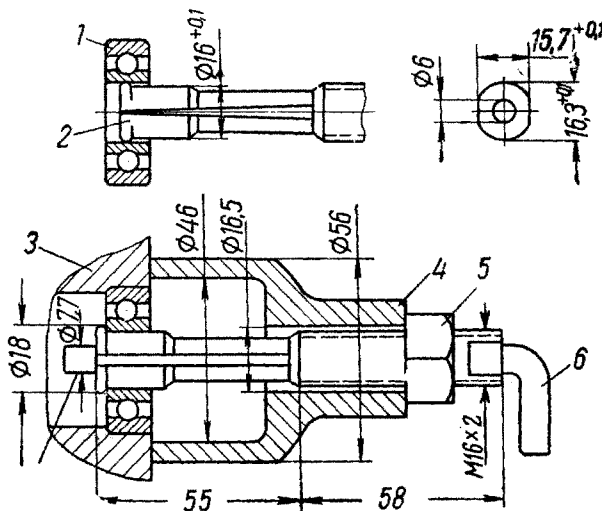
Приспособление для выпрессовки подшипника ведущего вала коробки передач:
